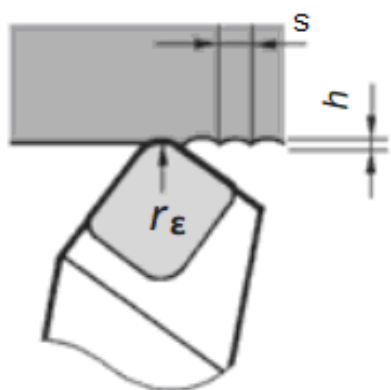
Схема образования шероховатости поверхности при точении [111]
